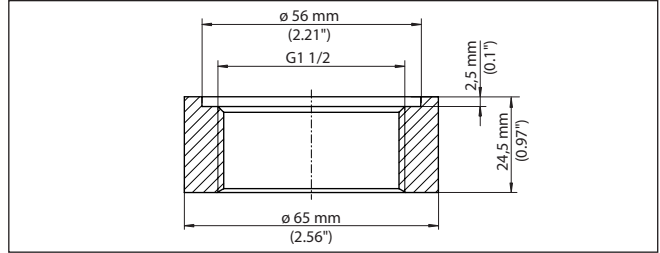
Maße Einschweißstutzen Gewinde G1½ (DIN 3852-A) - VEGABAR 82, 83, 86, 87
